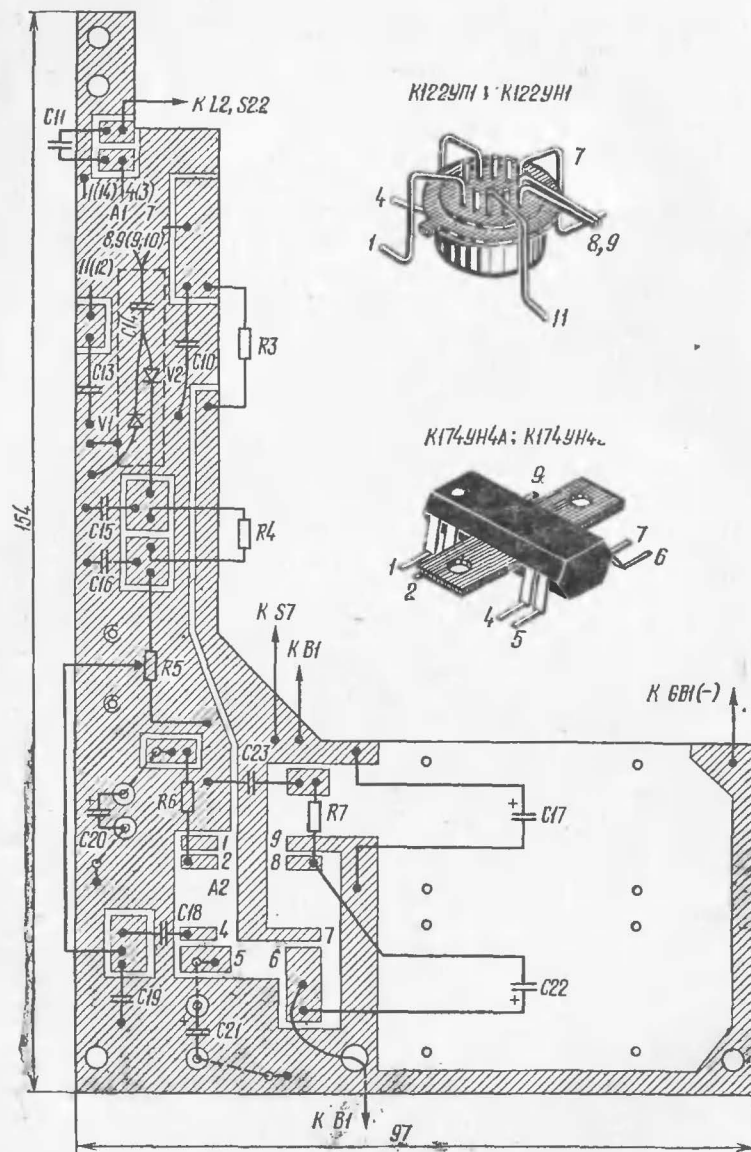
Чертеж печатной платы и размещение деталей на ней
